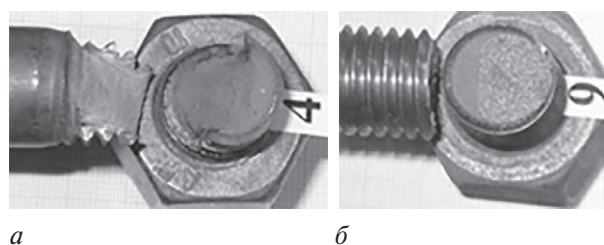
Примеры изломов в резьбовой части стержней болтов: а — пластичная (образец 4); б — хрупкая сталь (образец 9)
